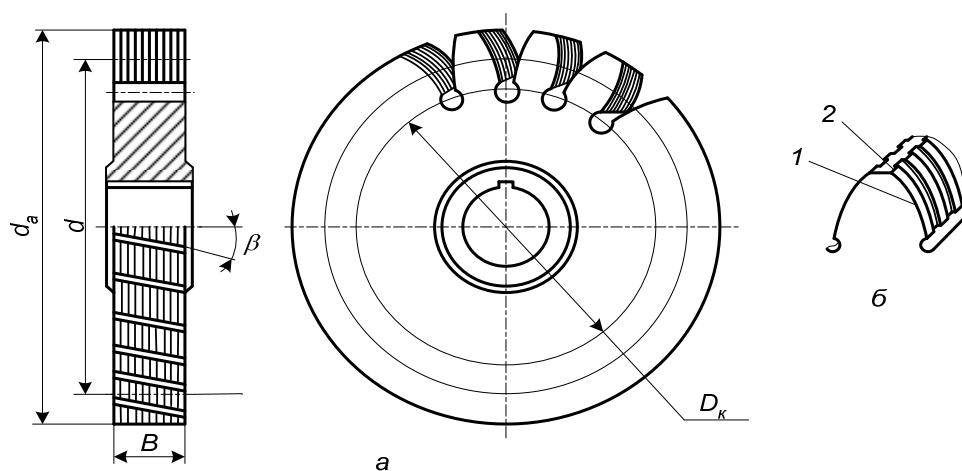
Дисковый шевер: а – общий вид шевера; б – форма канавок на зубе шевера
